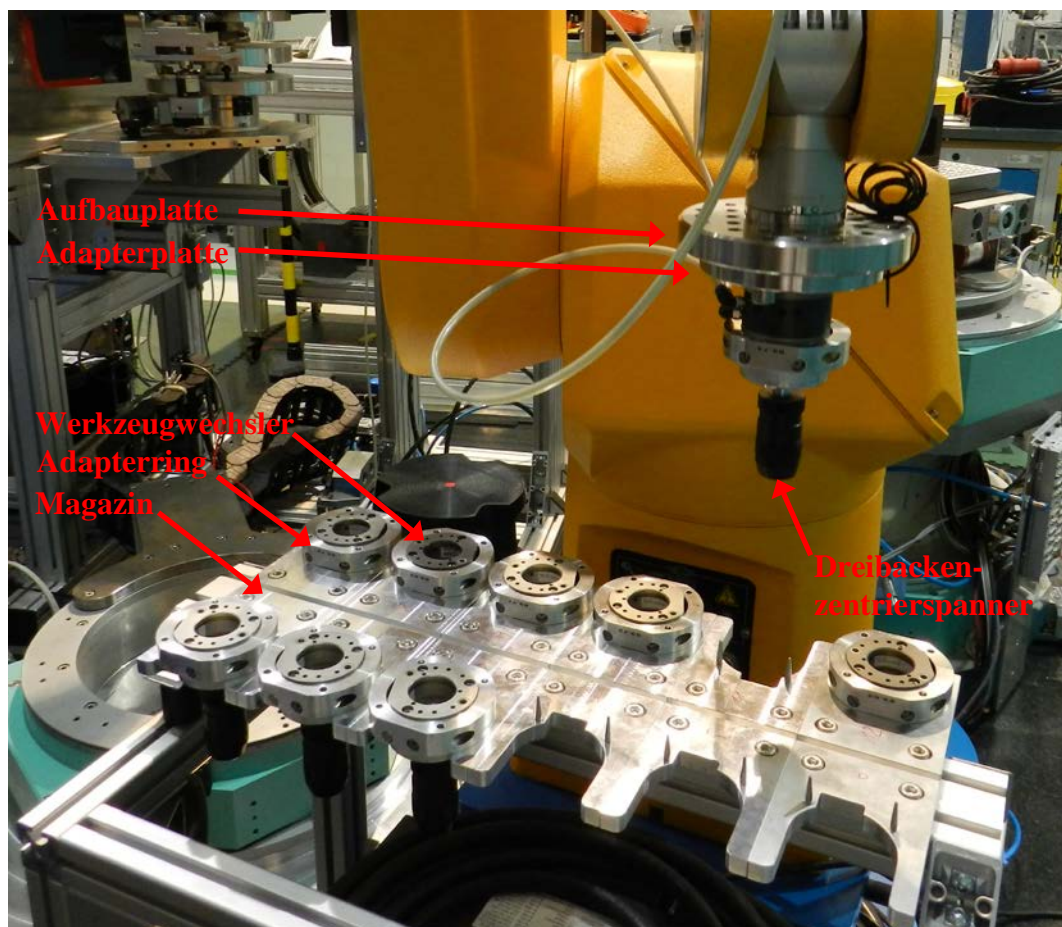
Zwölfach Probenwechsler des Roboters bestehend aus PTM Werkzeugwechslern und Dreibackenzentrierspannern für Texturserienmessungen.
